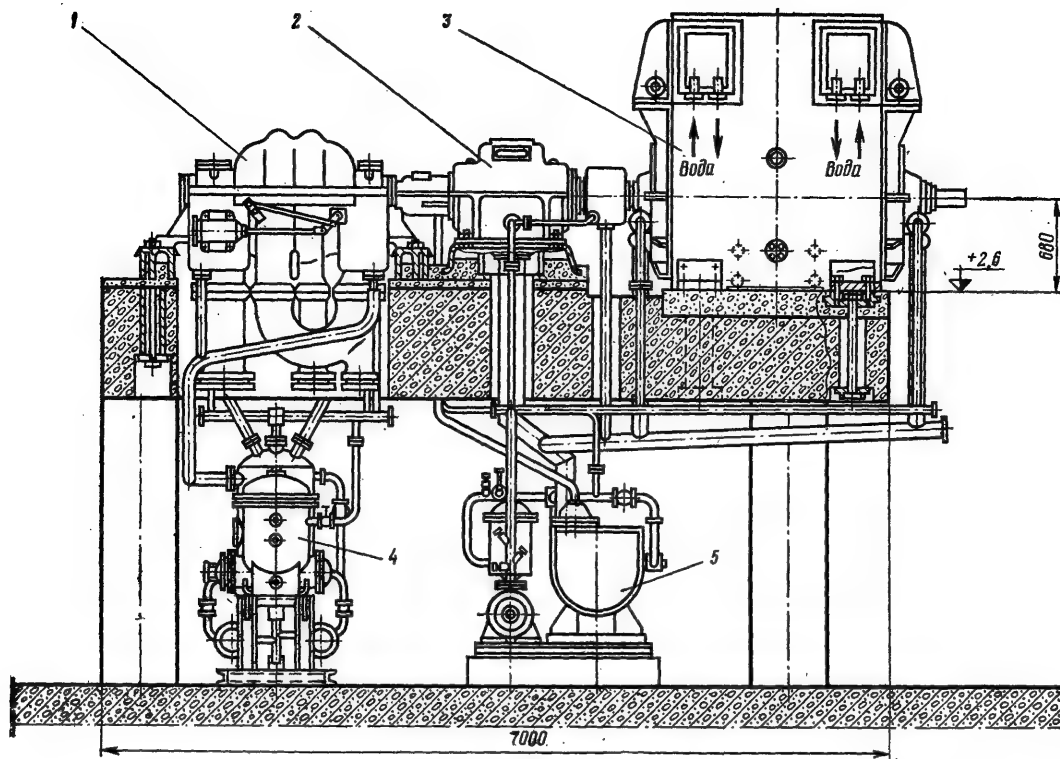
Пропановый центробежный холодильный агрегат АТКП-435-1600:
